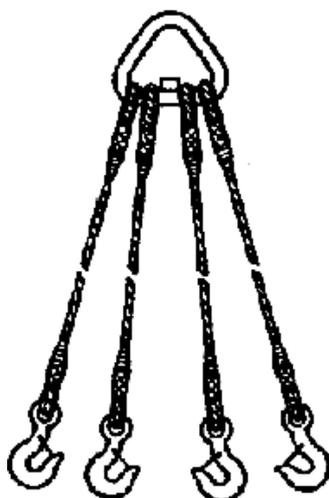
Строповочное приспособление типа 4СК1
